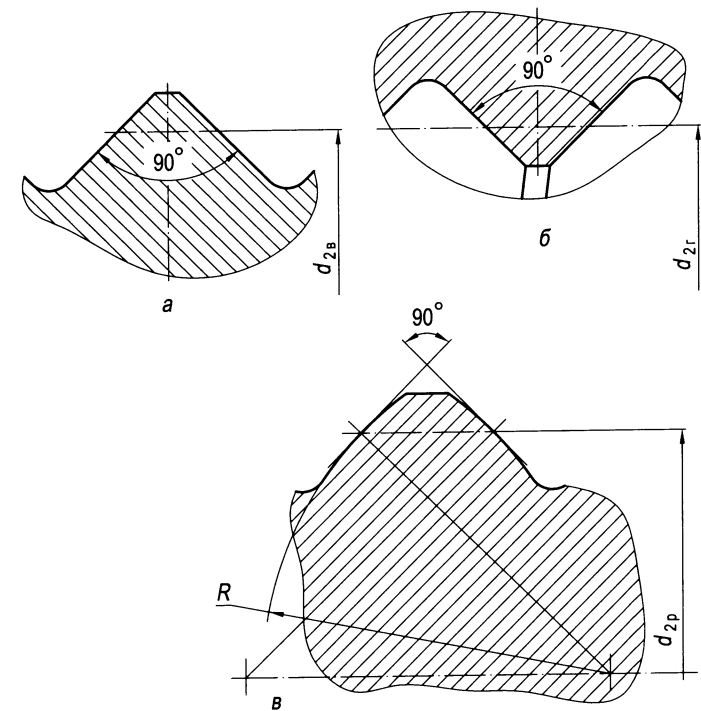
Профили резьбы винта (а), гайки (б) и ролика (в)
